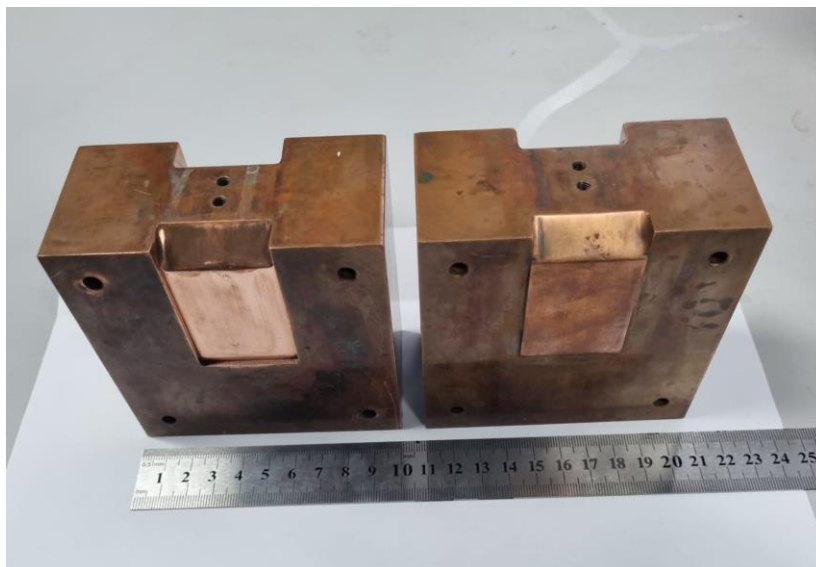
Molde de cobre que será utilizado na fundição centrífuga
